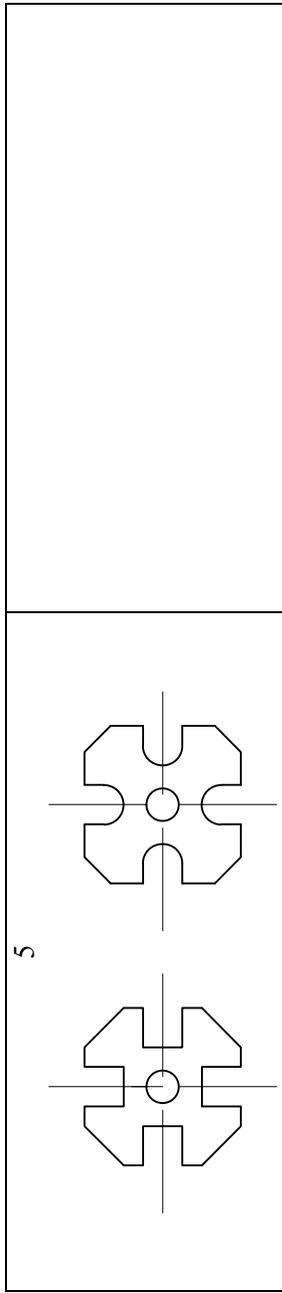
Примеры конструирования металлокерамических заготовок:
